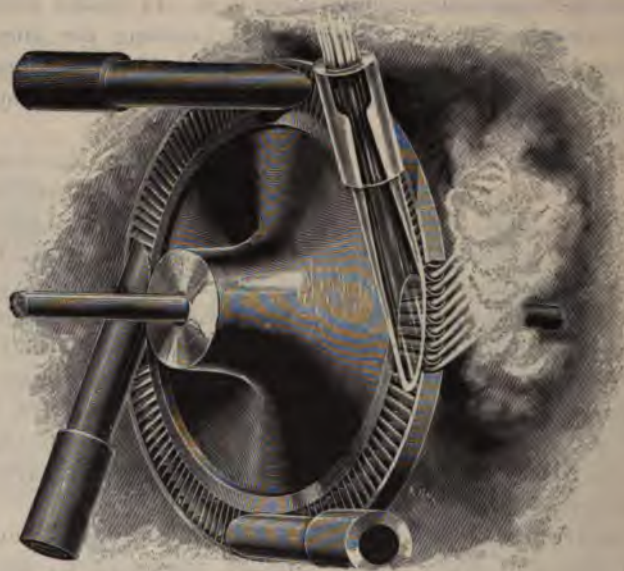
Lavalturbinenrad und Düsen. Maschinen-Fabrik Humboldt, Kalk b. Köln.
